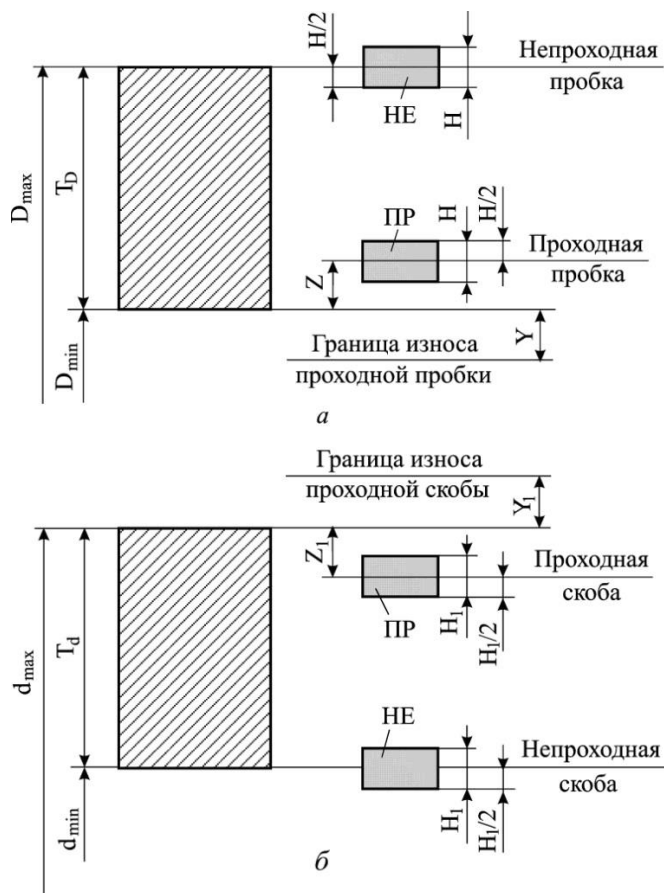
Схемы расположения интервалов допусков гладких калибров для контроля отверстий (а) и валов (б) с номинальными размерами до 180 мм и допуском изготовления по IT9-IT17
